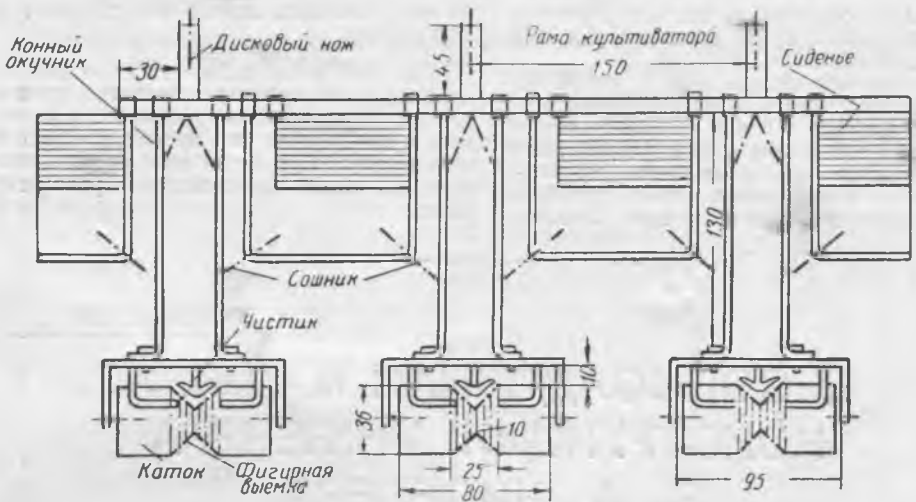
Схематический чертеж рабочих механизмов лесопосадочной машины конструкции В. А. Киселева.
